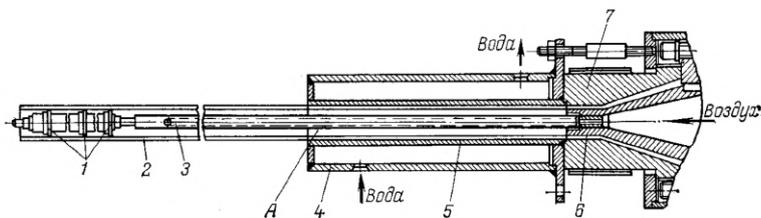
Устройство для калибровки труб по наружному диаметру:
